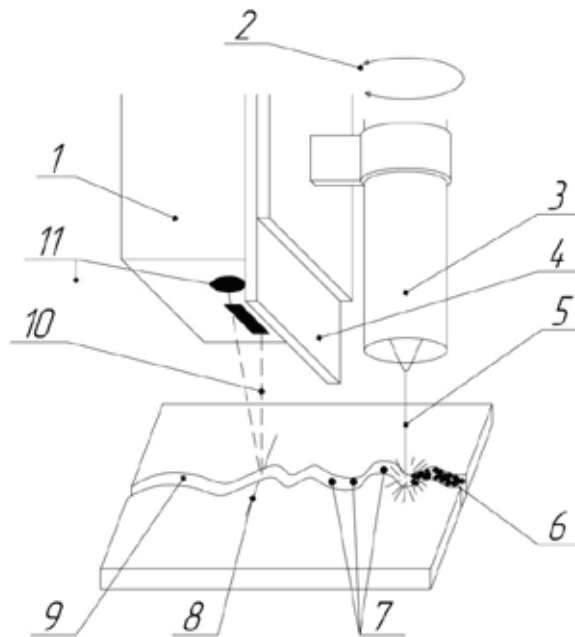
Схема работы системы: 1 — сенсор; 2 — вращение в запястье робота; 3 — сварочная головка; 4 — защитный экран; 5 — сварочная проволока 6 — сварочный шов; 7 — позиция коррекции; 8 — линия сканирования 9 — стык свариваемых деталей; 10 — сканирующий луч; 11 — камера
